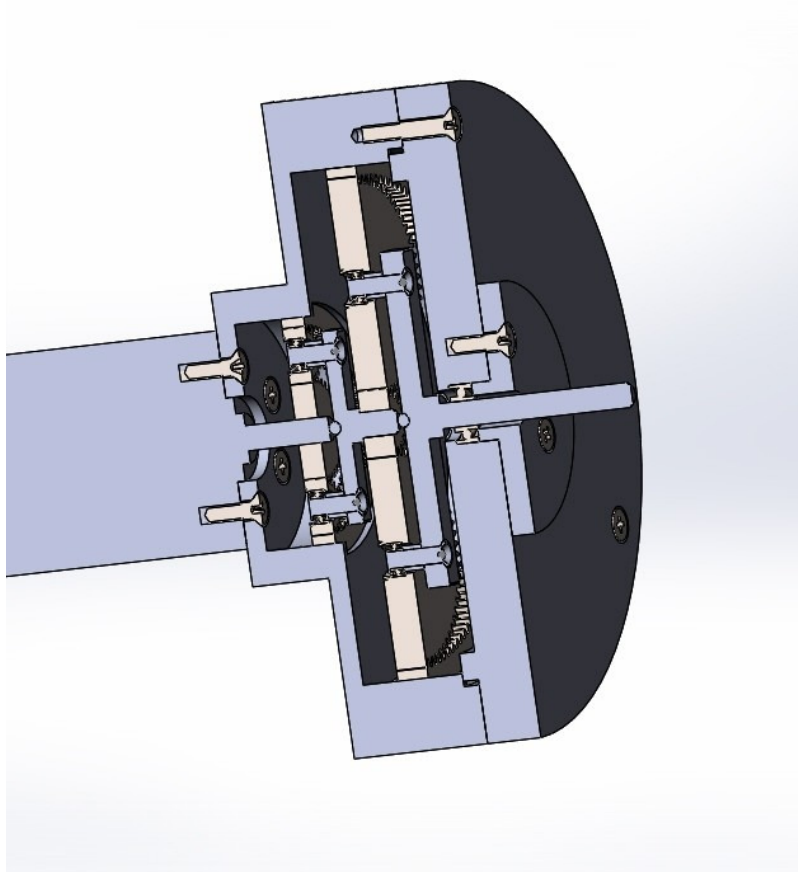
Двухступенчатый редуктор привода управления тормозом
